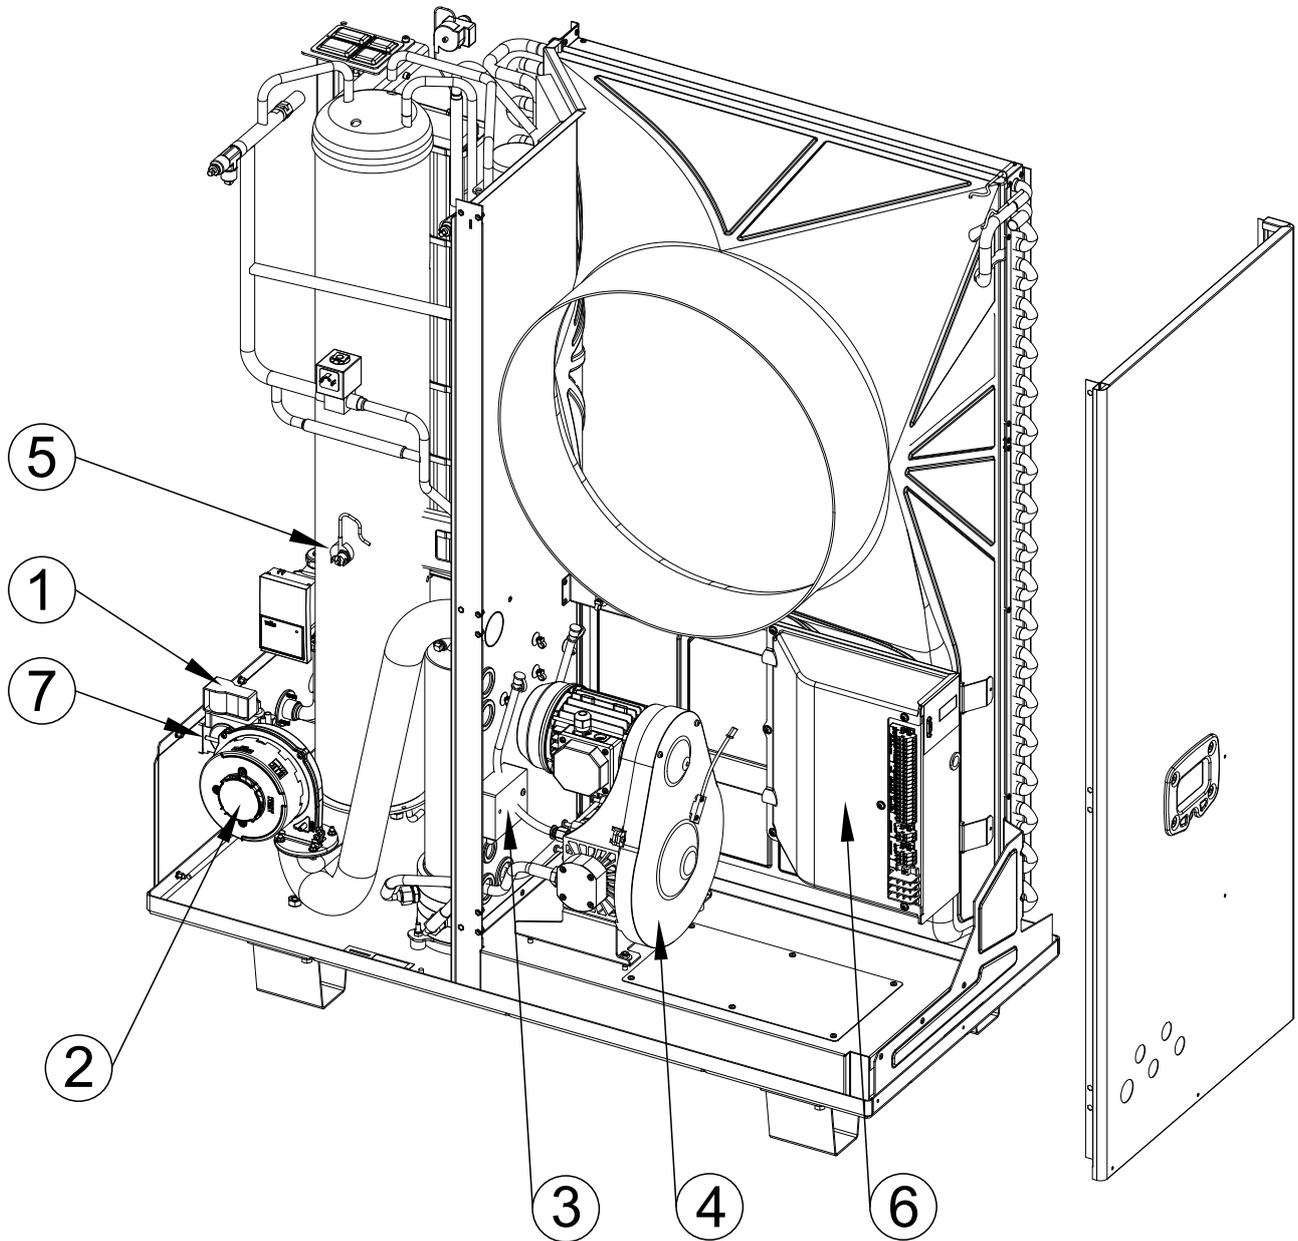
Interne Komponenten Wärmepumpenmodul Rückansicht
